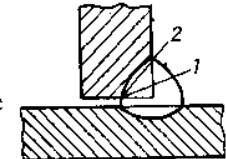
Схема расчетных сечений сварного соединения с угловым швом:
